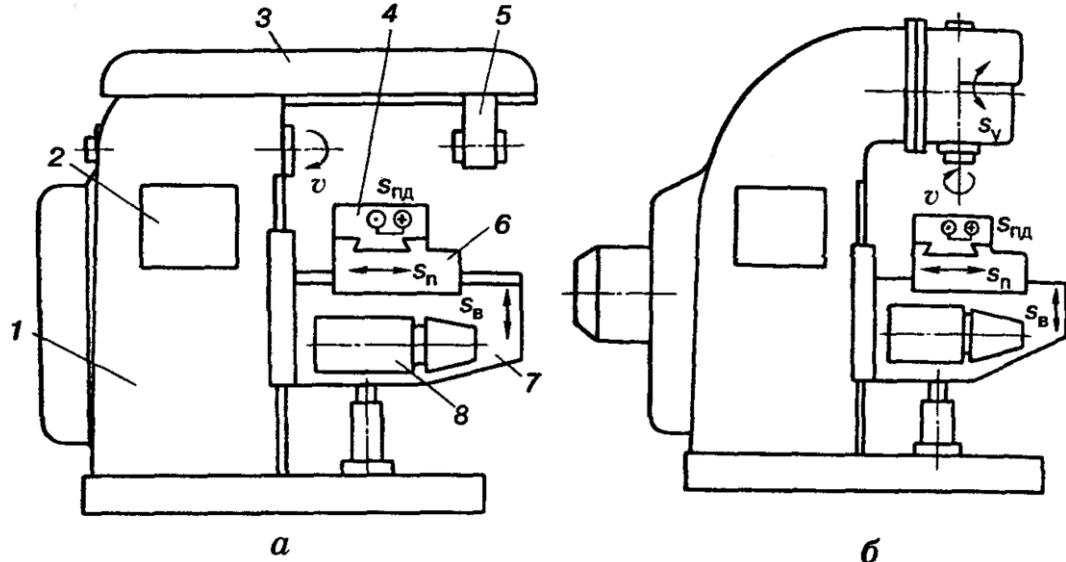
Консольні горизонтально-фрезерний і вертикально-фрезерний верстати
